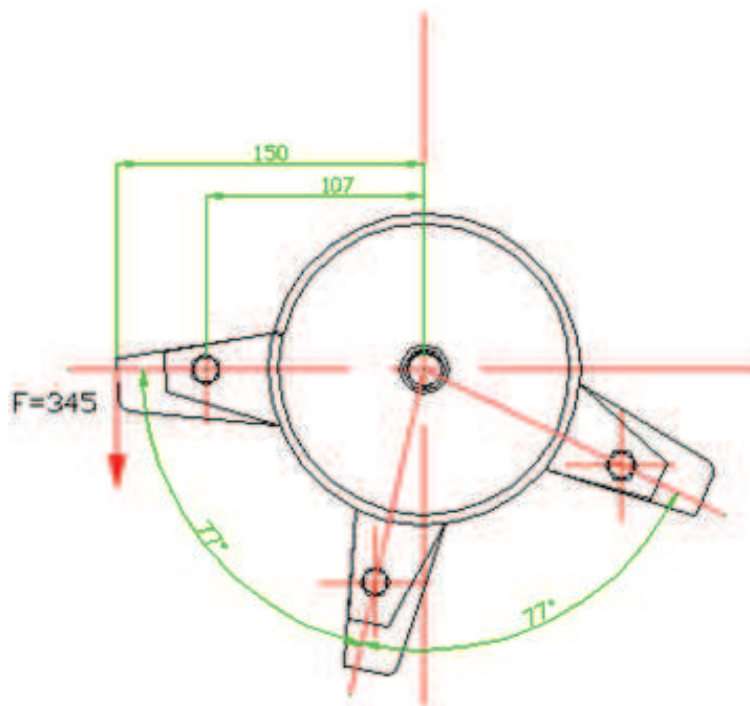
Dimensiones desde el centro del cilindro a la fuerza de corte
